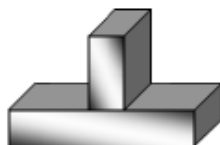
Soldadura de canto e soldadura de canto em T [4]
